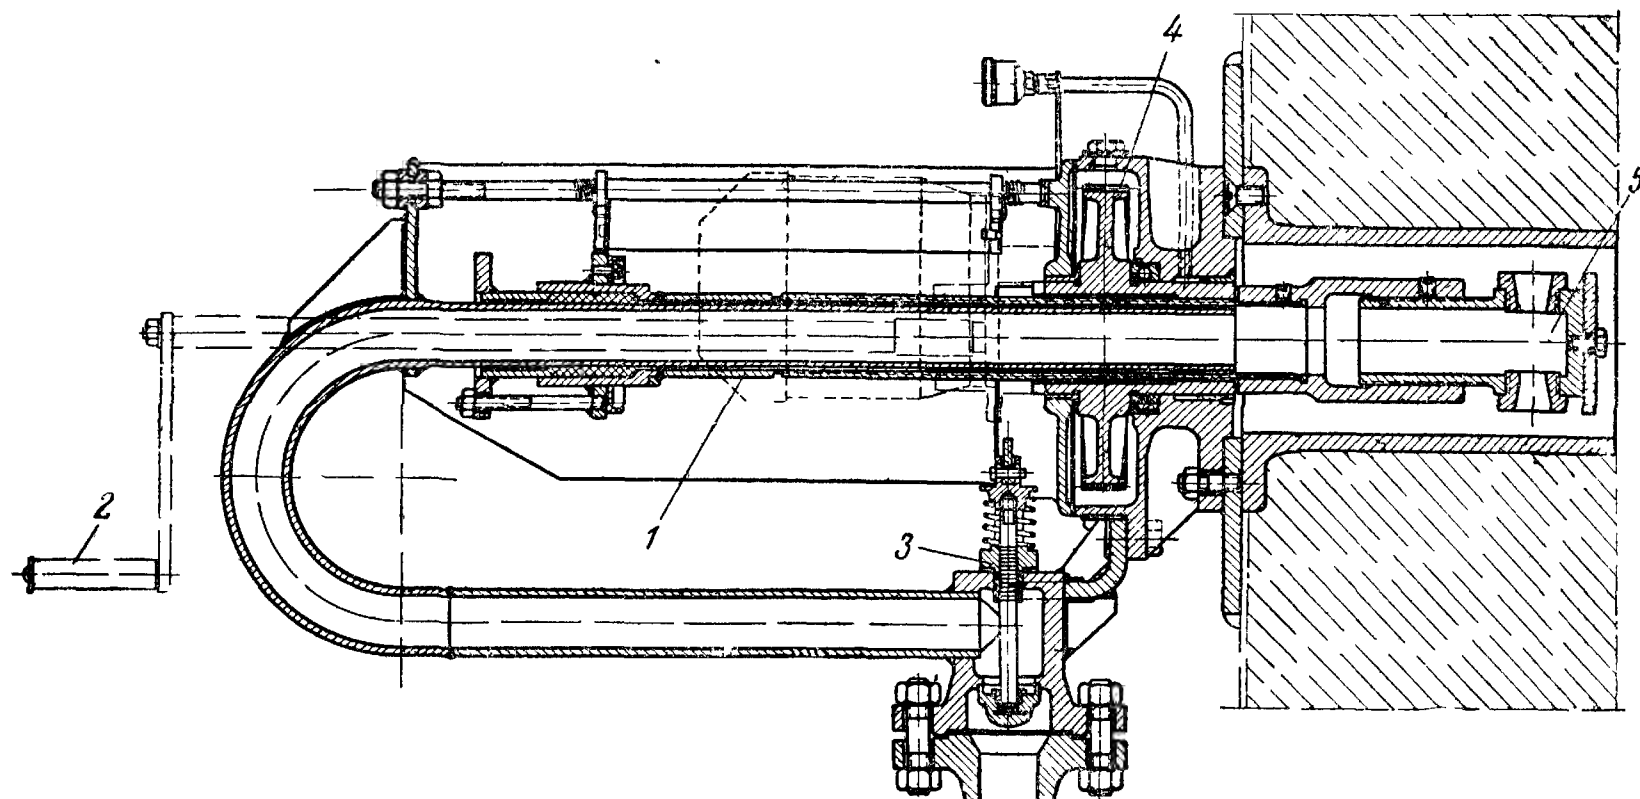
Обдувочный прибор Ильмарине—ЦКТИ для обдувки экранных поверхностей нагрева.
